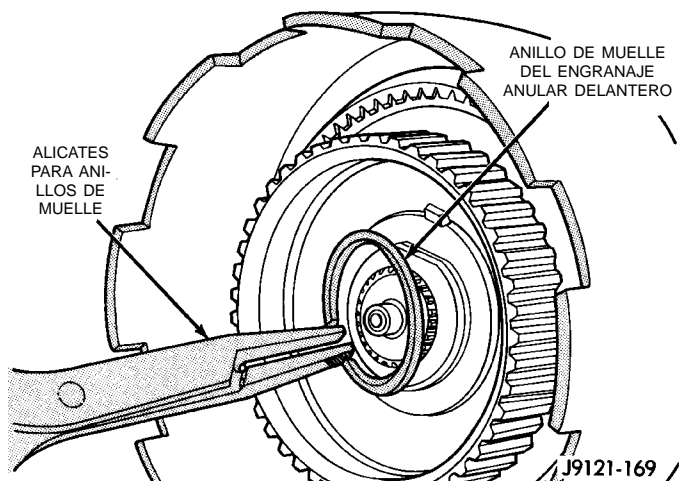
Instalación del anillo de muelle del engranaje anular delantero
